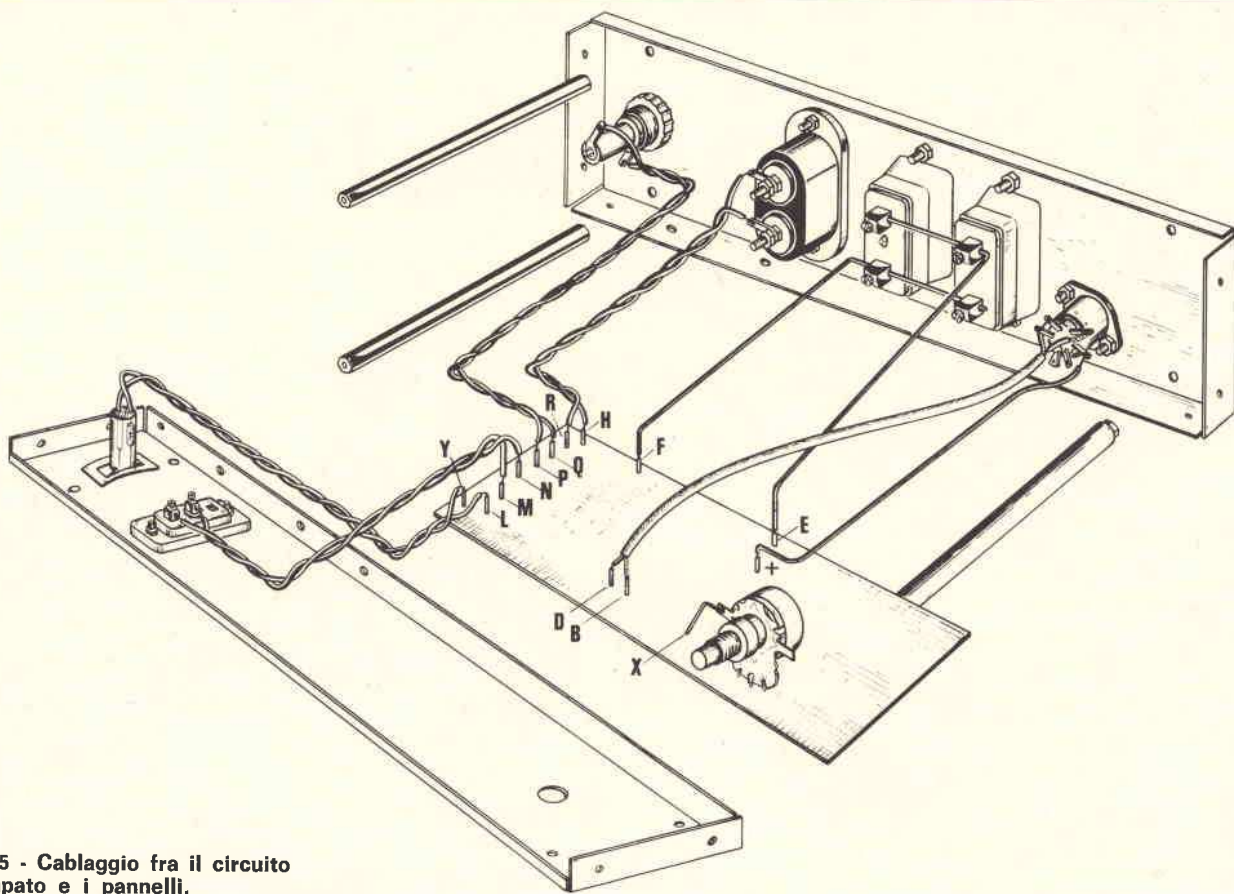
Cablaggio fra il circuito stampato e i pannelli.
